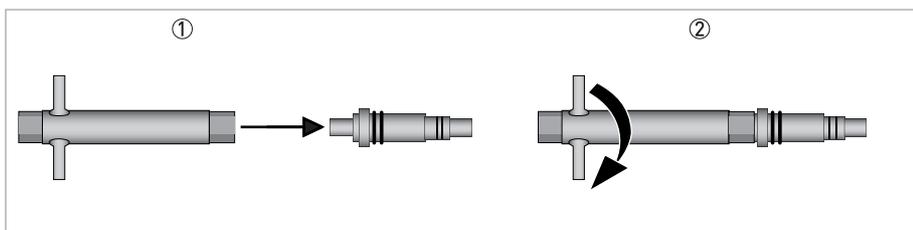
Установка измерительного преобразователя в инструмент
